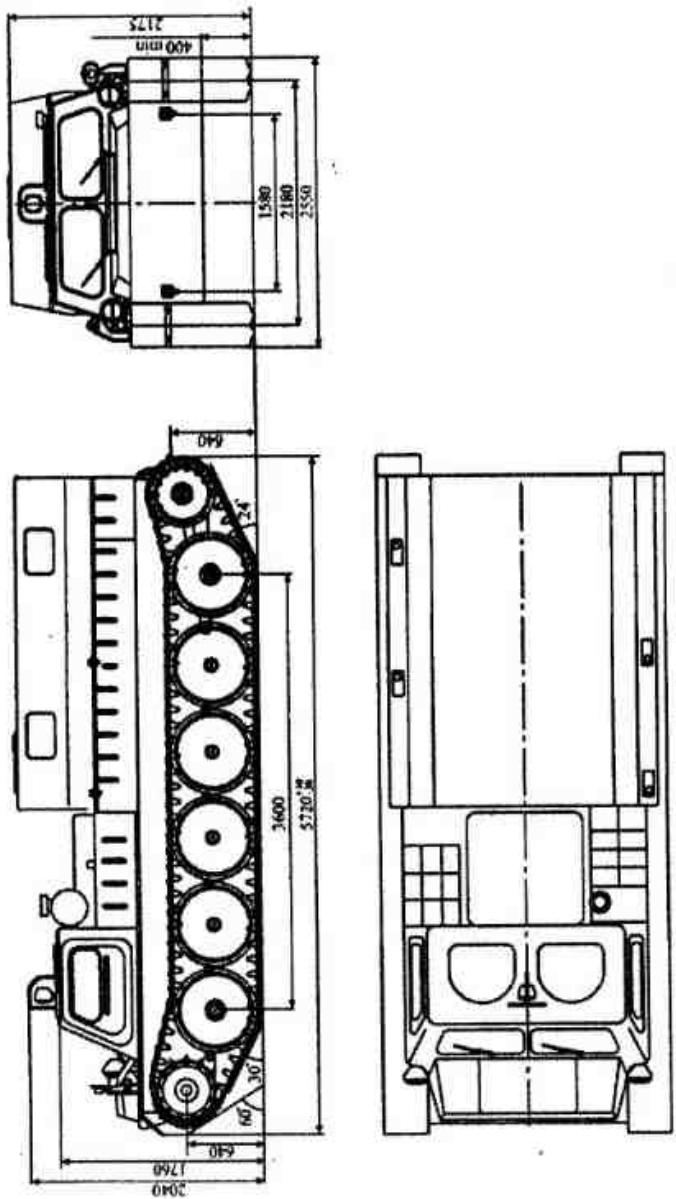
Габаритные размеры снегоболотохода ГАЗ-34039 (34039-0000032 / 033)
